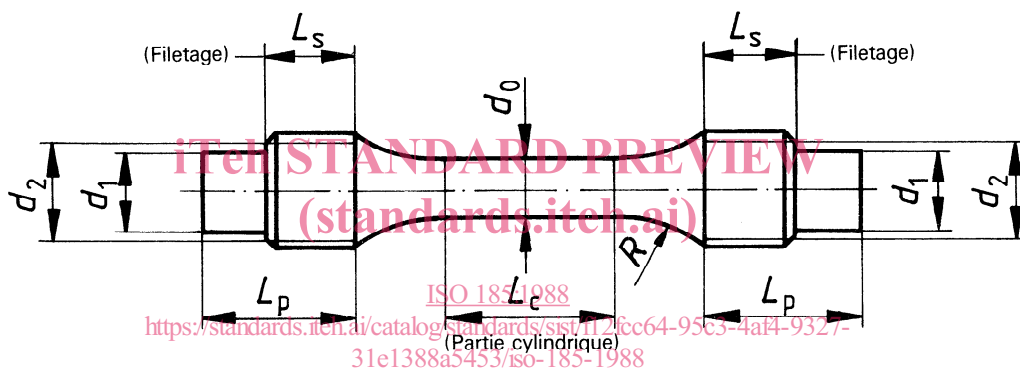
Éprouvette A¹⁾Figure 5 — Éprouvette B¹⁾
